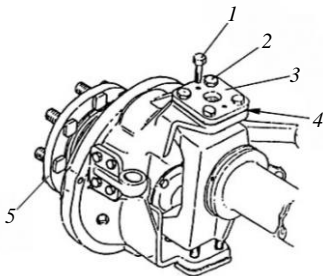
Регулировка подшипников осей шкворня: 1 – демонтажный болт; 2 – болт; 3 – ось; 4 – регулировочные прокладки; 5 – фланец
